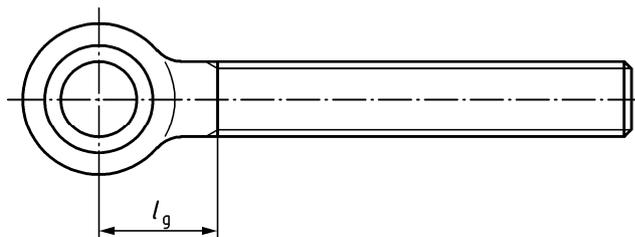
Augenschrauben mit Gewinde annähernd bis Auge
